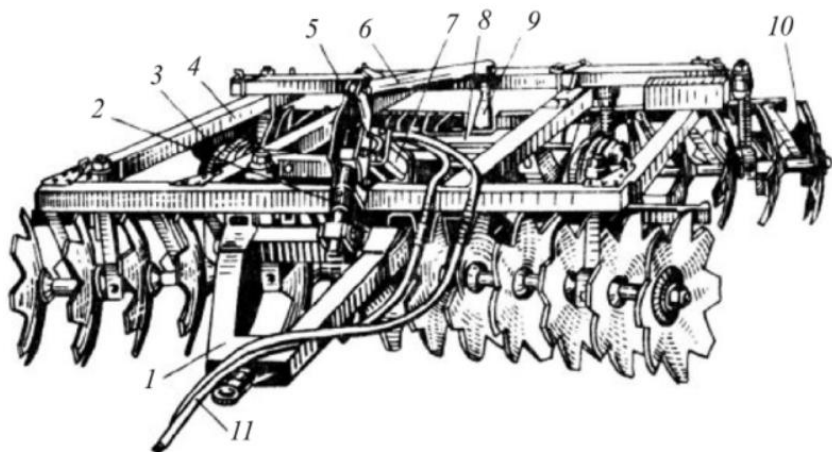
Борона дисковая тяжелая БДТ-3,0: 1 — прицеп; 2 — регулировочный винт; 3 — колесо; 4 — рама; 5 — рычаг; 6 — механизм выравнивания рамы; 7 — гидроцилиндр перевода бороны в транспортное положение; 8 — коленчатая ось; 9 — кулак; 10 — чистики; 11 — шланг высокого давления.
